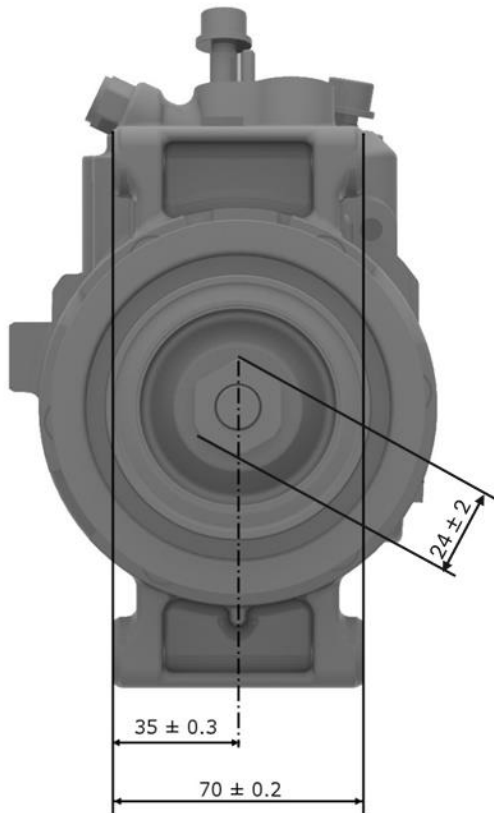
Размеры компрессора климатической установки (вид спереди)
